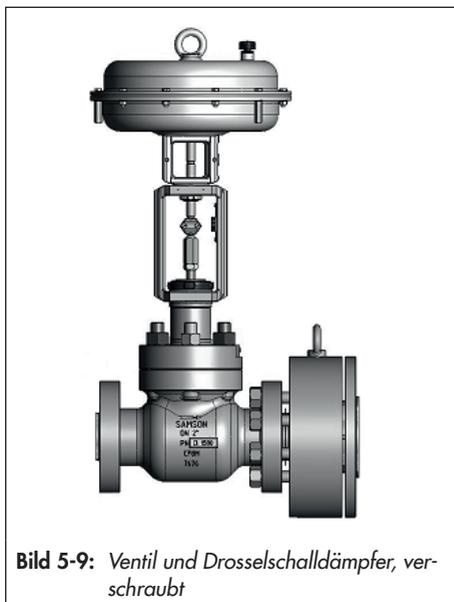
Ventil und Drosselschalldämpfer, verschraubt
